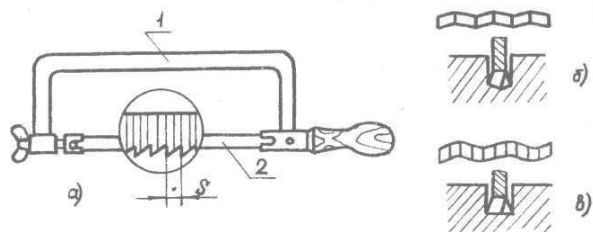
Ножовочный станок и виды разводки зубьев ножовочного полотна.
